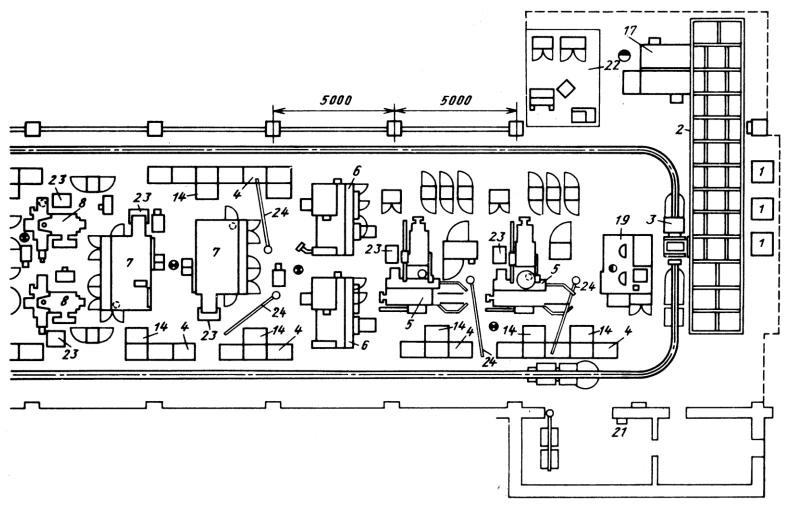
Планировка ГПС ACB-201 для изготовления корпусных деталей в мелко- и среднесерийном производстве (правая часть)
